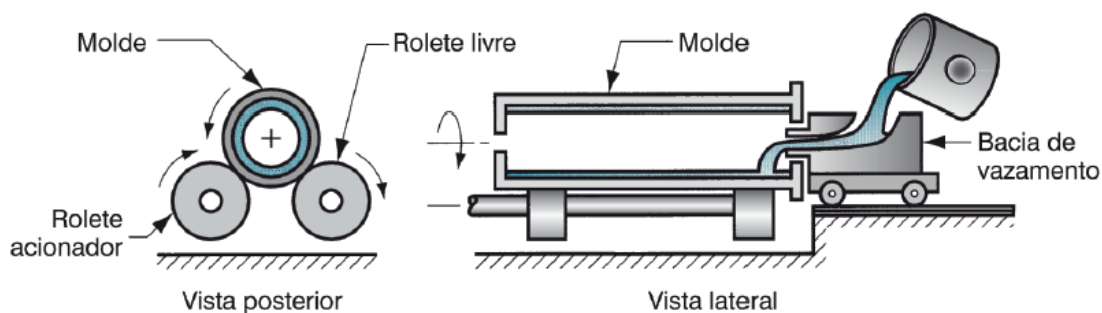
Sistema utilizado no equipamento de fundição centrífuga horizontal [13].
